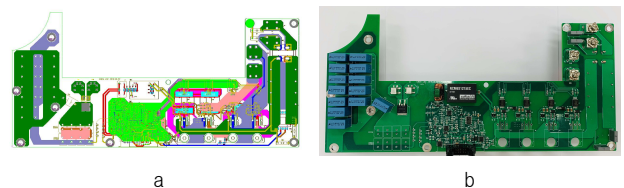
kW급 전기자동차용 LDC PCB 아트웍 (a)와 시제품 (b) 사진
